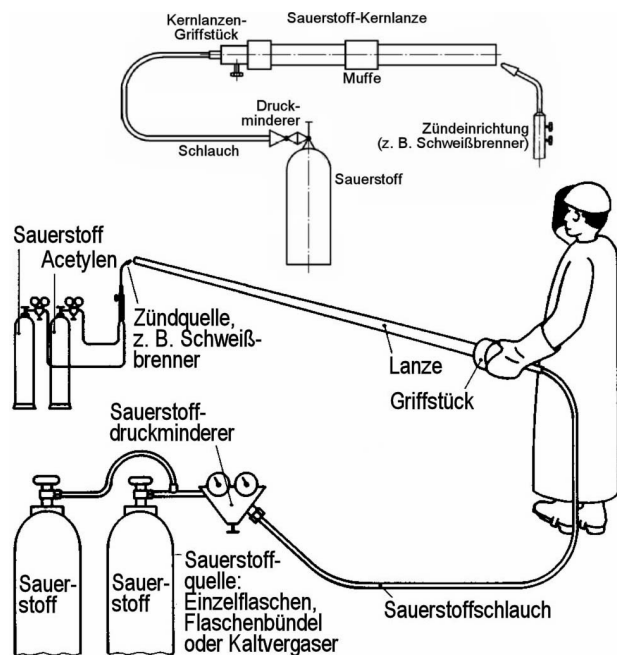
Grundausrüstung zum Betreiben einer Sauerstoff-Kernlanze.
